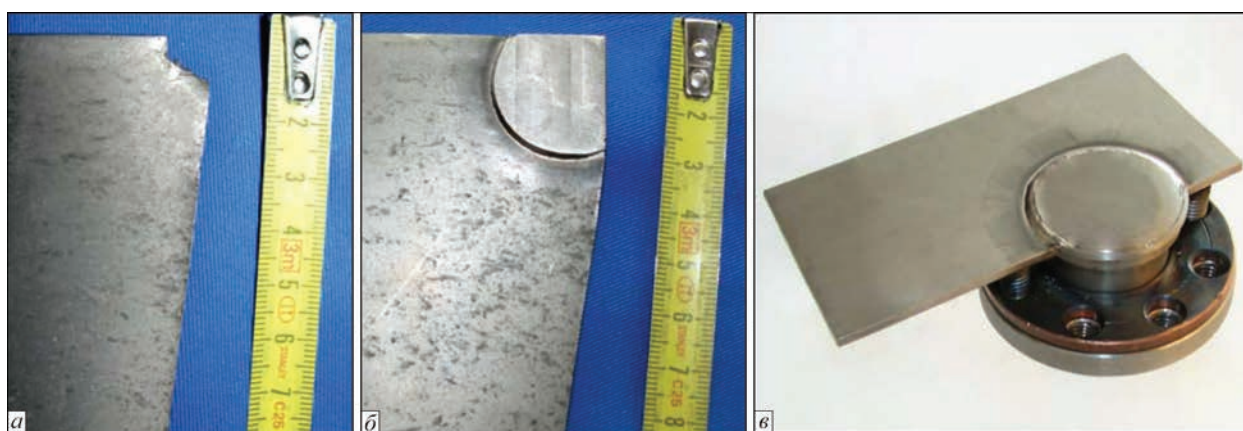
Ремонт точечных дефектов угла пера лопатки с применением цилиндрических ремонтных «вварышей»: а — поврежденный угол лопатки до ремонта; б — отремонтированный угол (края «вварыша» обрезаны после ЭЛС); в — сборочно-сварочная оснастка для ЭЛС цилиндрических «вварышей» (имитатор лопатки)
